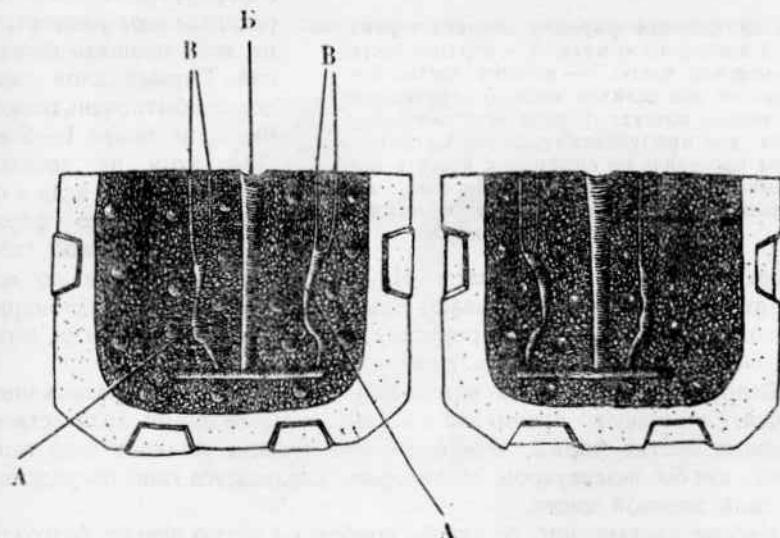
Клеевая форма и отливка черепа. Раскрыта форма для отливки "под давлением" приборов (скелетных косточек). А — прибор, В — литник, В — воздушки.
